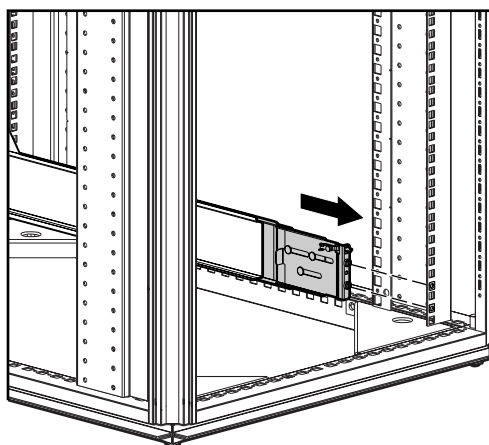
Inserimento della parte posteriore della guida sinistra nel rack
